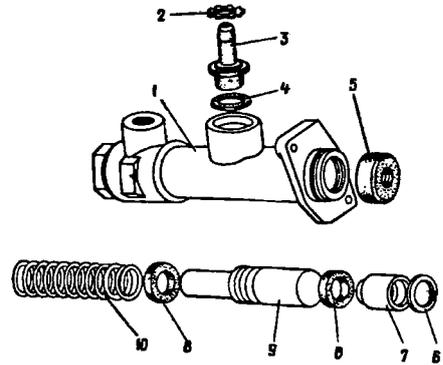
Детали главного цилиндра: 1 - корпус; 2 - стопорная шайба; 3 - штуцер; 4 - прокладка; 5 - колпачок; 6 - стопорное кольцо; 7 - поршень толкателя; 8 - уплотнительное кольцо; 9 - поршень главного цилиндра; 10 - пружина
